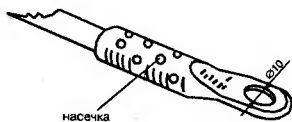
Конструкция клеммы вторичной обмотки сварочного аппарата
